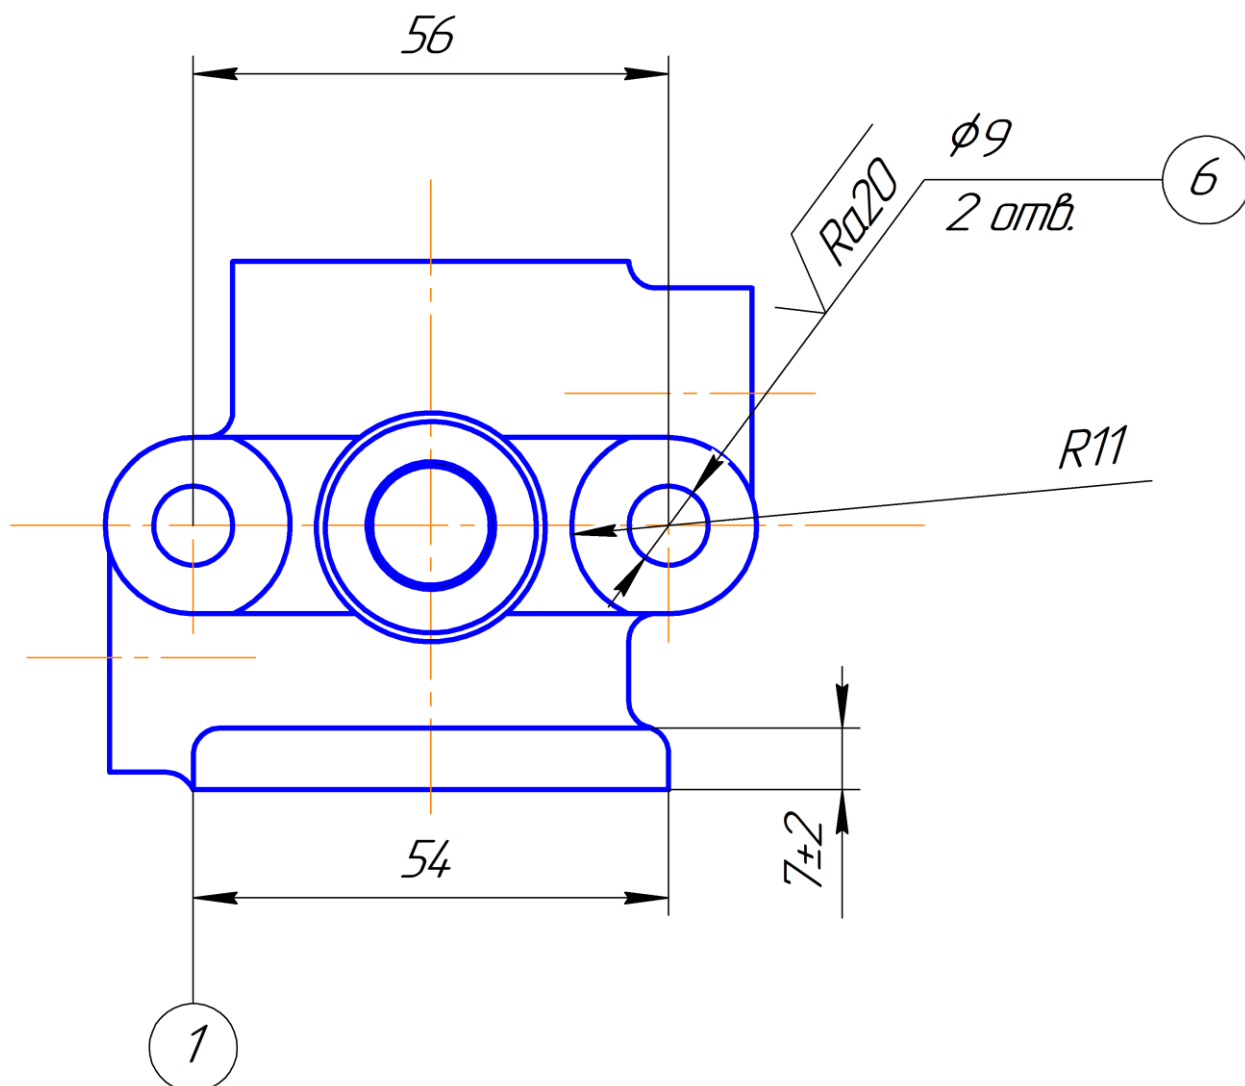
Вид А по чертежу. Нумерация поверхностей детали.
